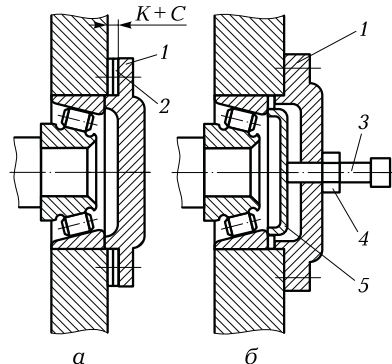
Схема регулировки подшипниковых узлов с роликовыми радиально-упорными подшипниками:
